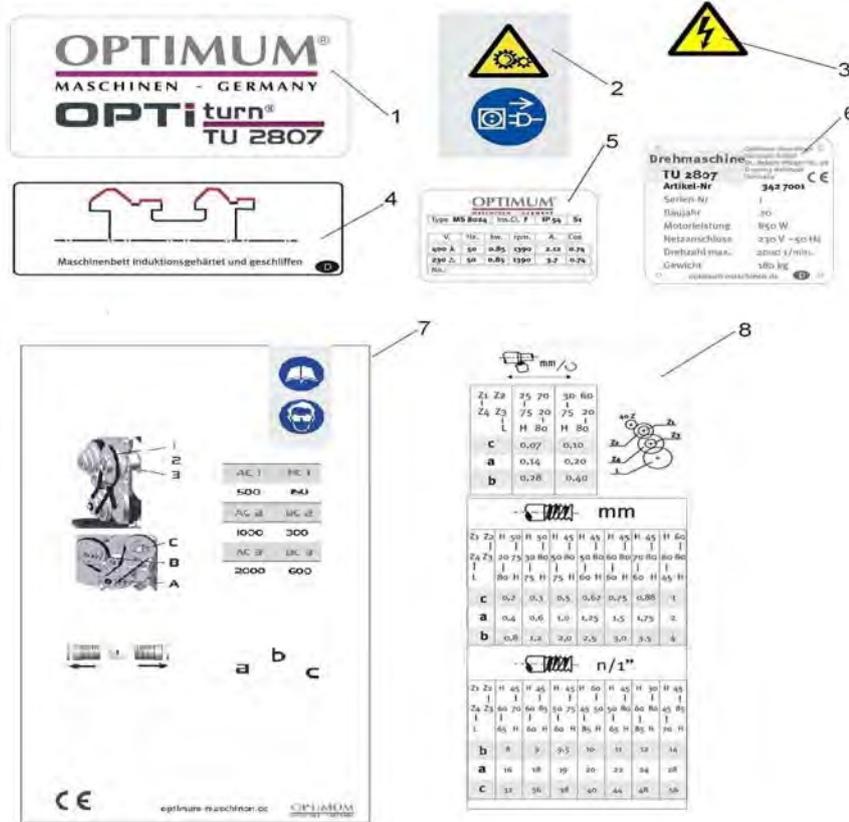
Maschinenschilder - Etiquetas de la máquina
